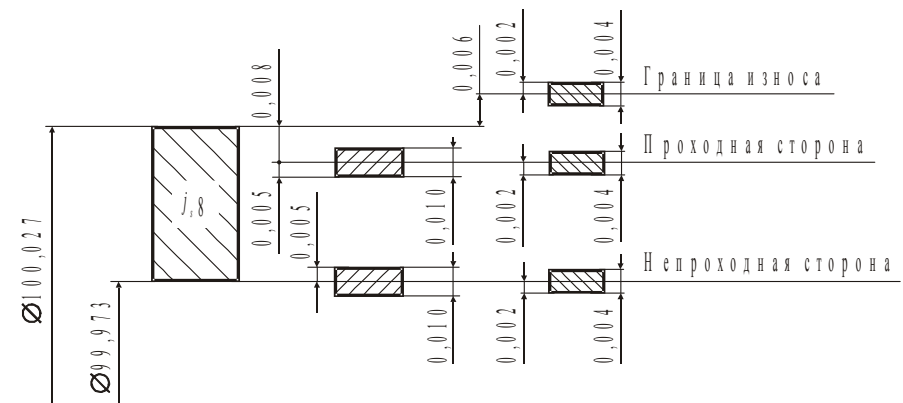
Схема расположения полей допусков калибров для контроля вала Ø100 j,8
